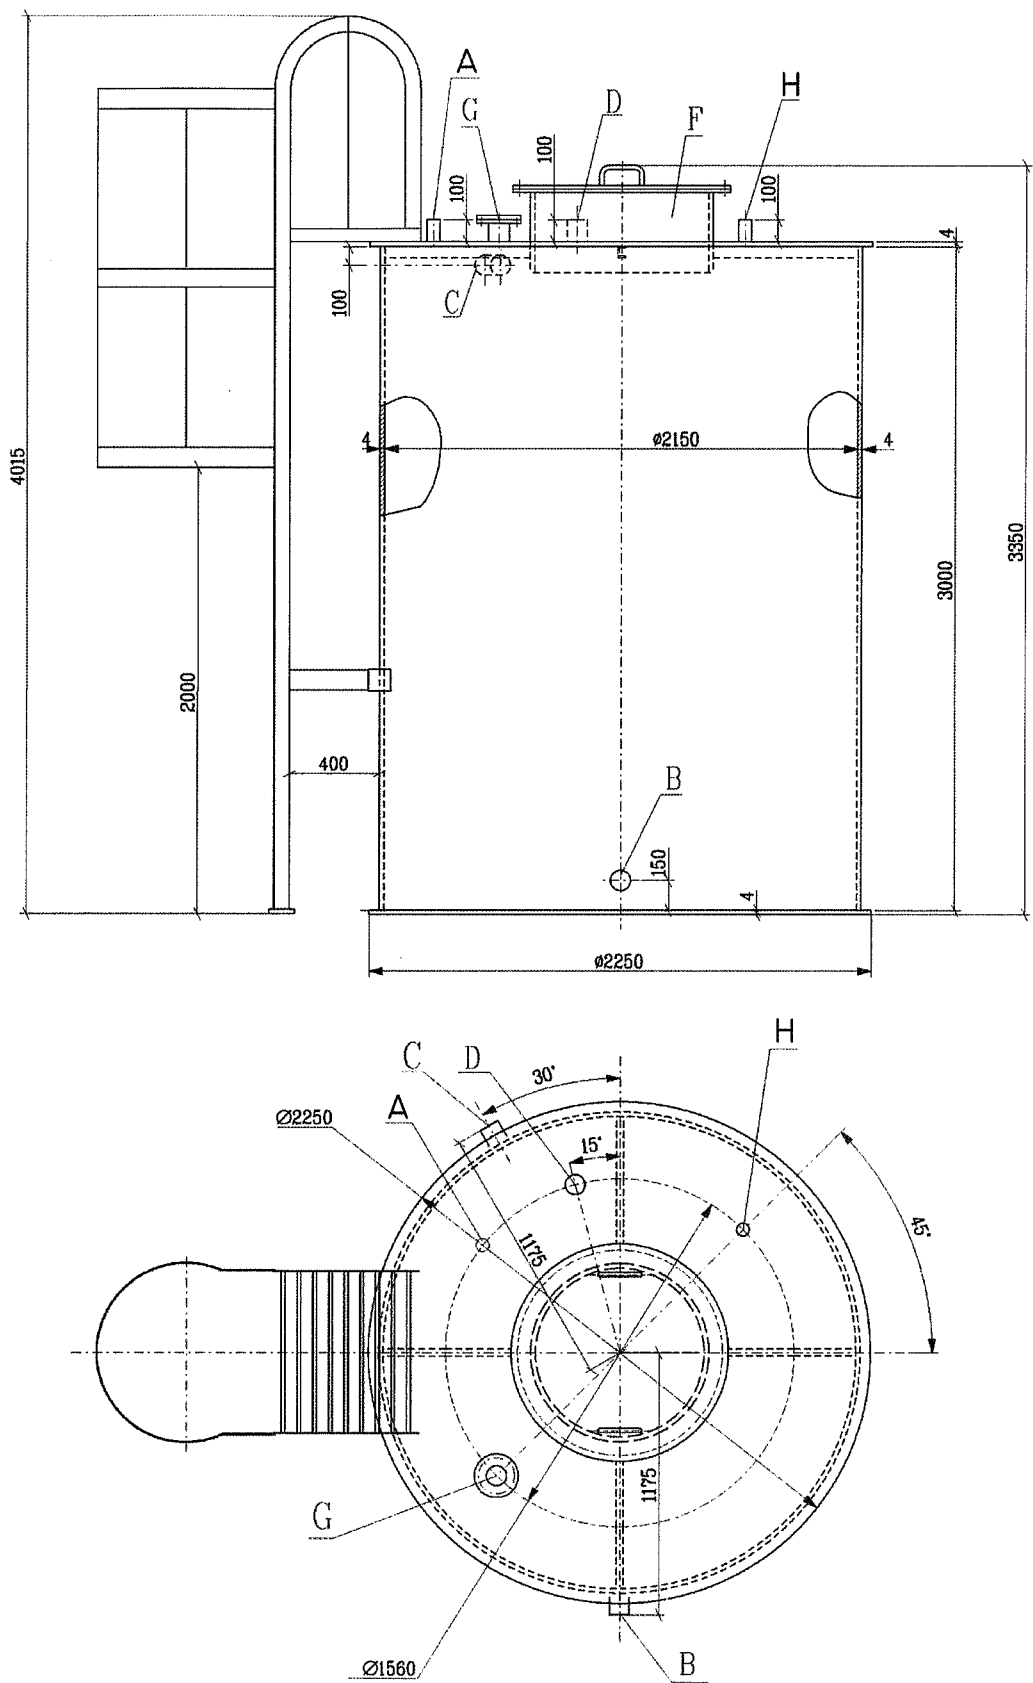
Габаритный чертеж мерника аммиака LDN40BB001, LDN40BB002
